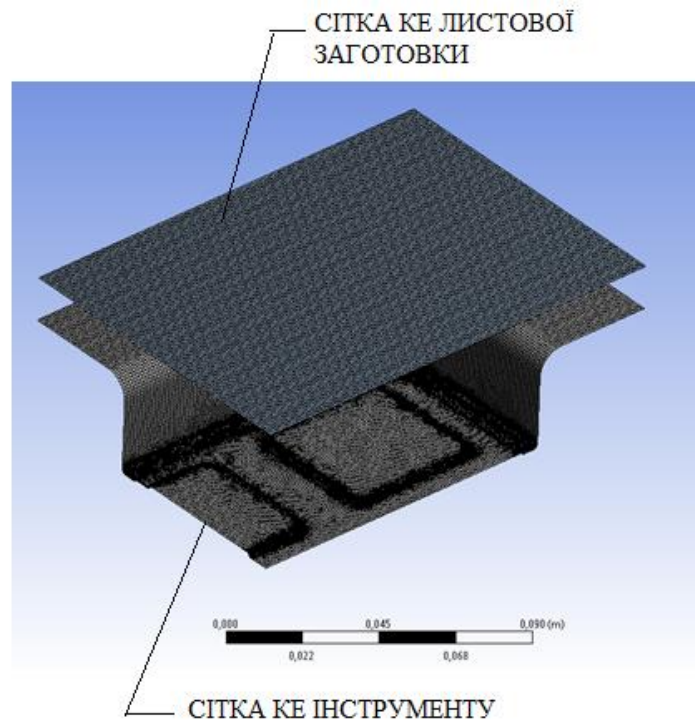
Сітка кінцевих елементів інструменту та заготовки
